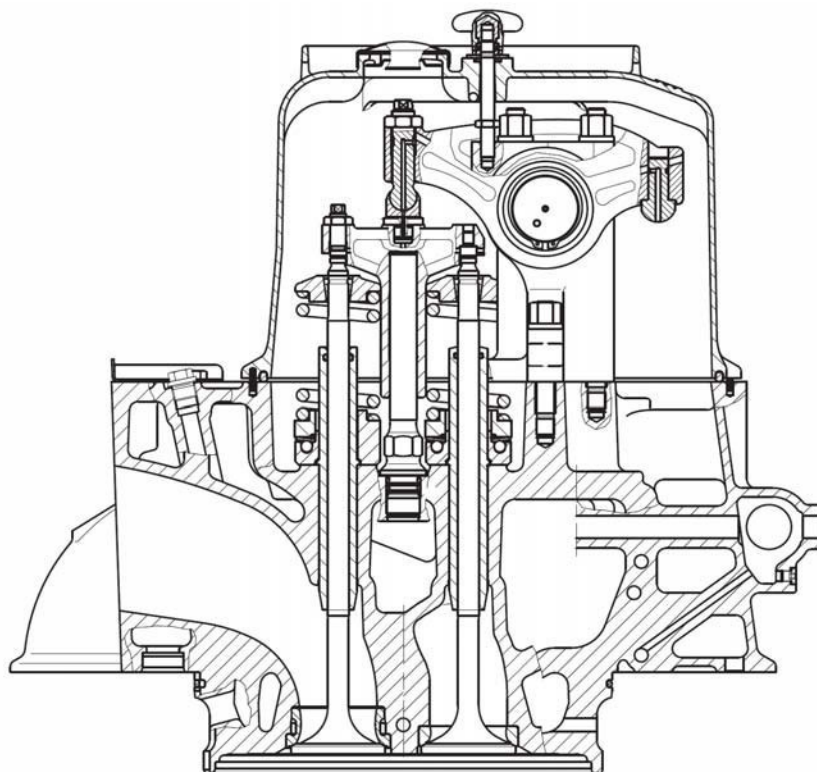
Кришка циліндру з механізмом газорозподілу суднового дизеля МаК 32С
